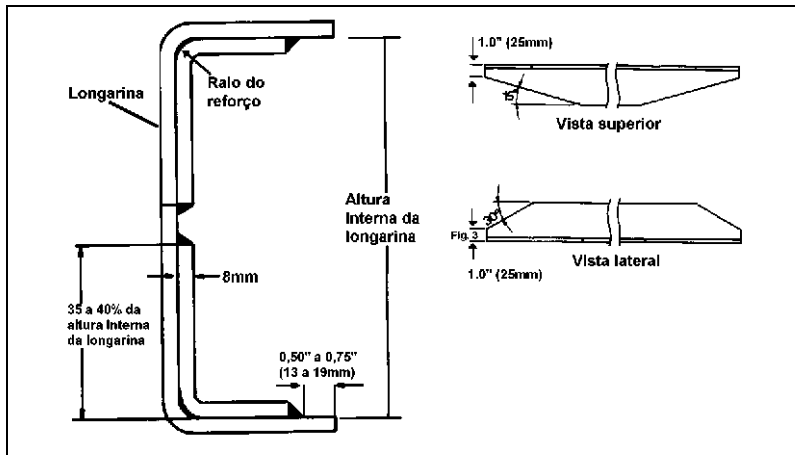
Fijación de los refuerzos mediante soldadura
